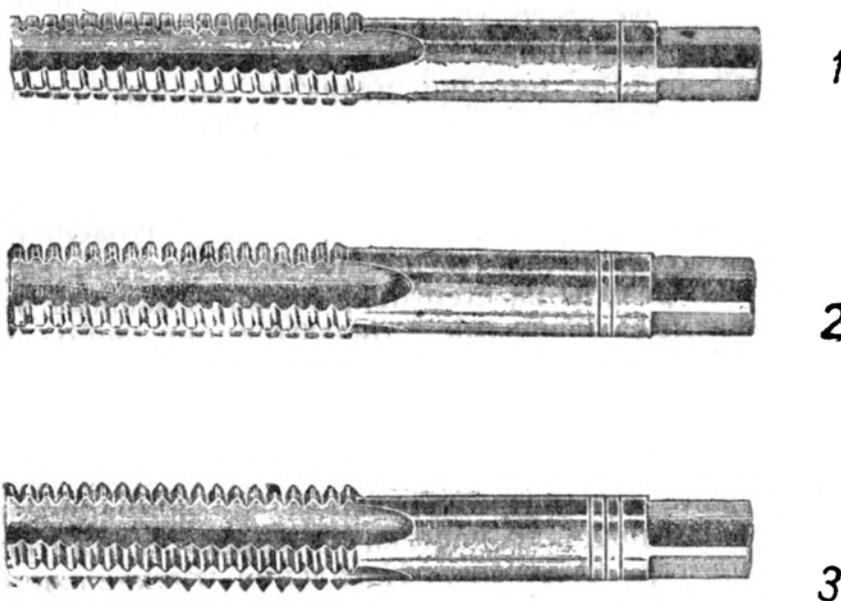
Набор метчиков: 1—черновой; 2—получистовой; 3—чистовой
